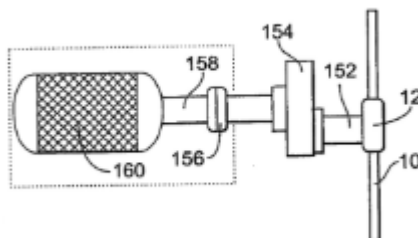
Dibujo de la patente EP1805412. Fuente: EP1805412, Stephen Dewar, Turbine and compressor employing tubercle leading edge rotor design, 2016
